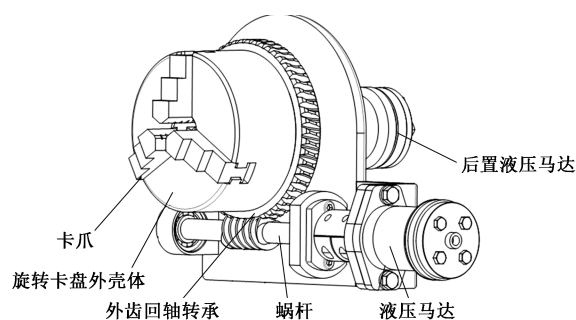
旋转卡盘机构(无机构装配外壳)结构示意图
